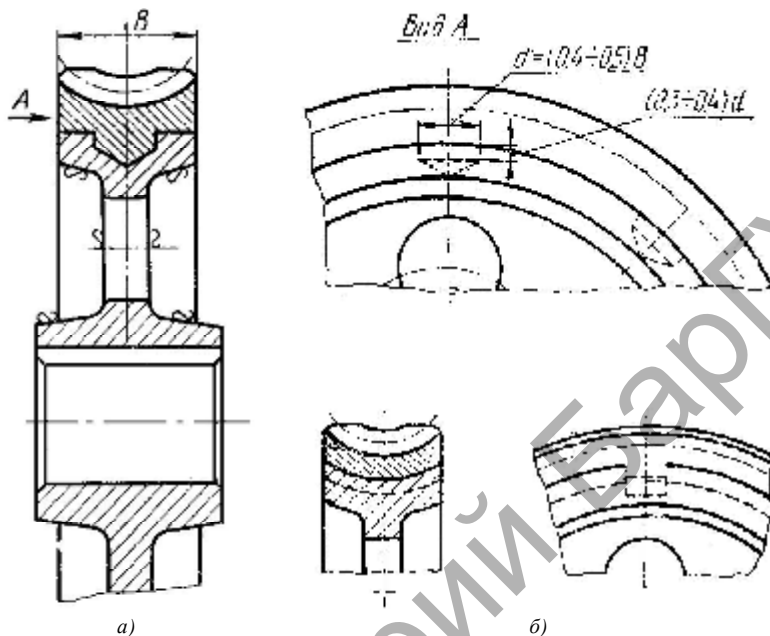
Биметаллическая конструкция червячного колеса [18]
